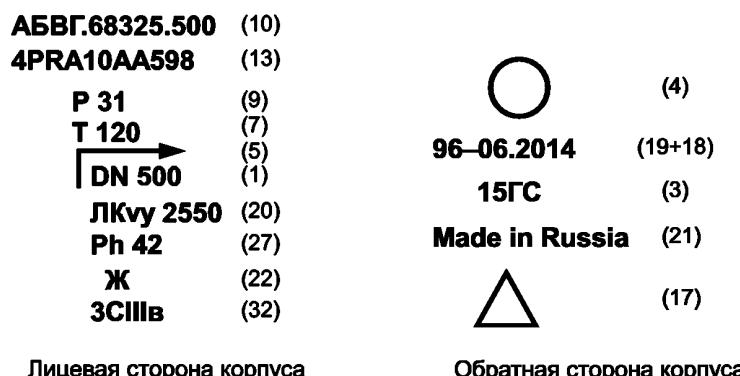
Пример расположения маркировки на корпусе углового регулирующего клапана
